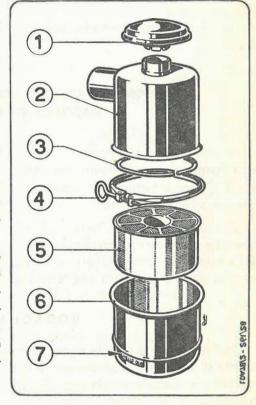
SMONTAGGIO DEL FILTRO ARIA
